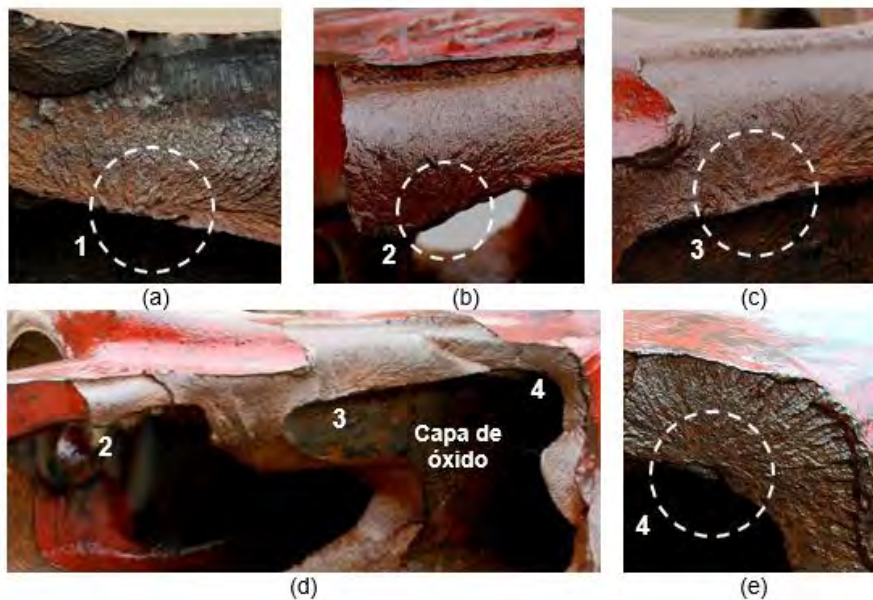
Detalle de origen de Fisura 1 (a), Fisura 2 (b), Fisura 3 (c) y Fisura 4 (e); y ubicación de fisuras en superficie de fractura del lado izquierdo (d).
